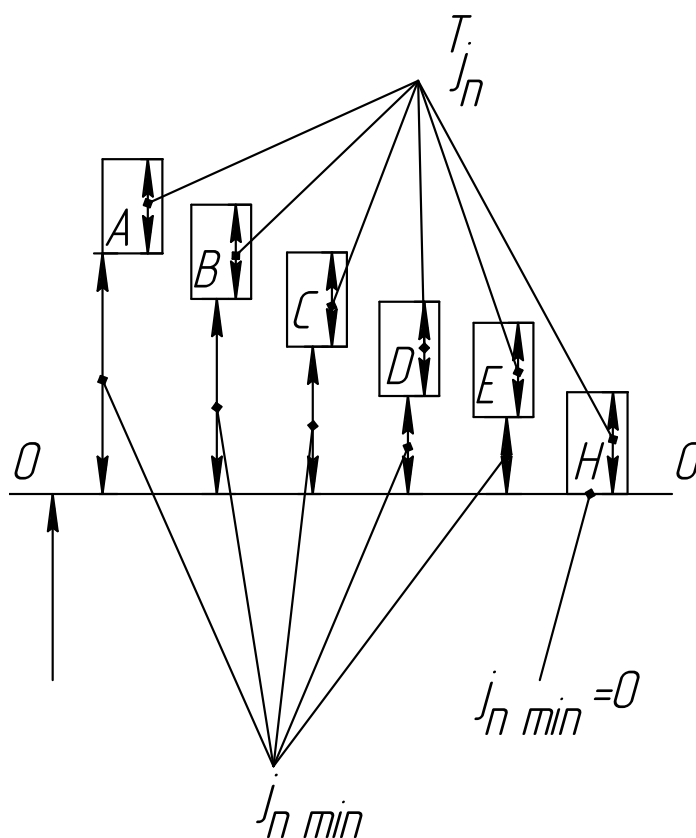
Виды сопряжений зубьев зубчатых колес
